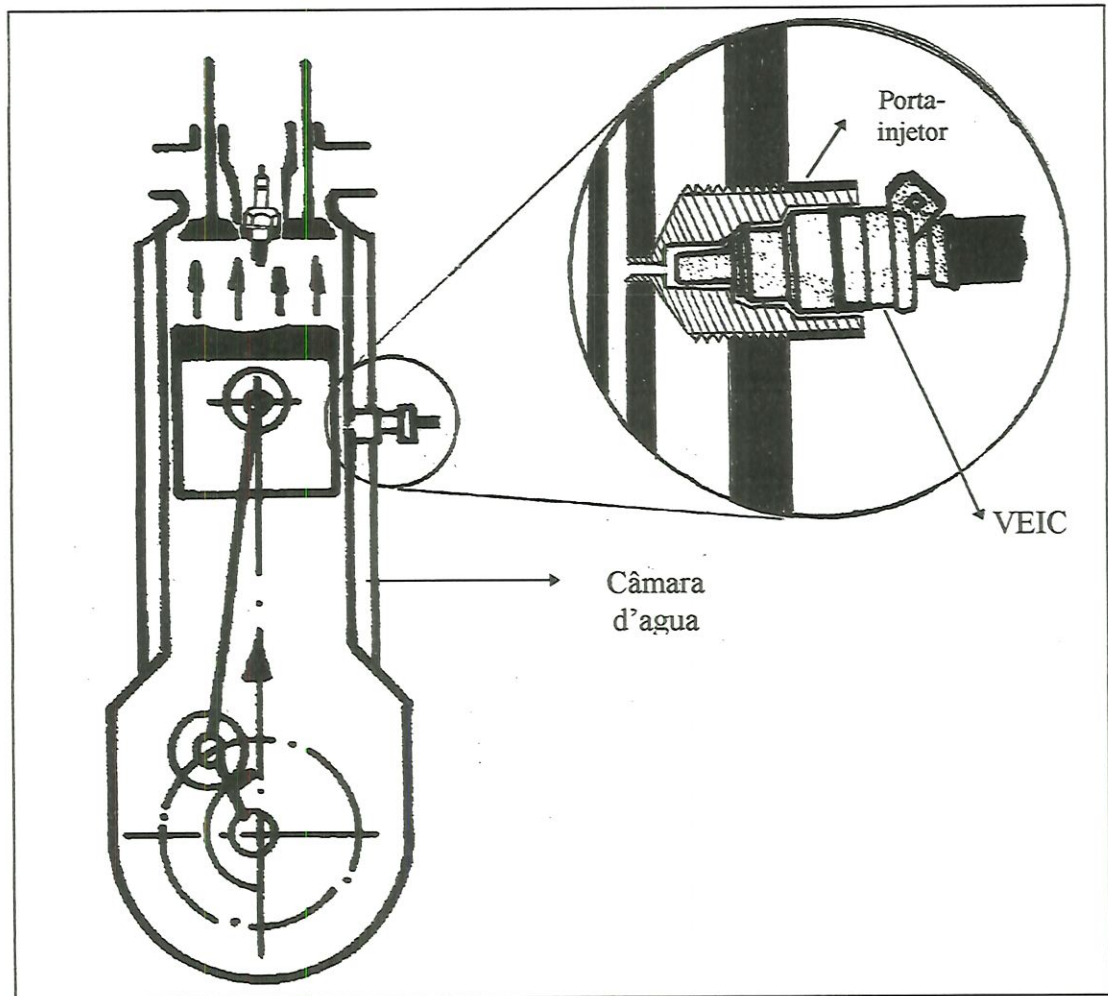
Corte esquemático da instalação do porta-injetor
